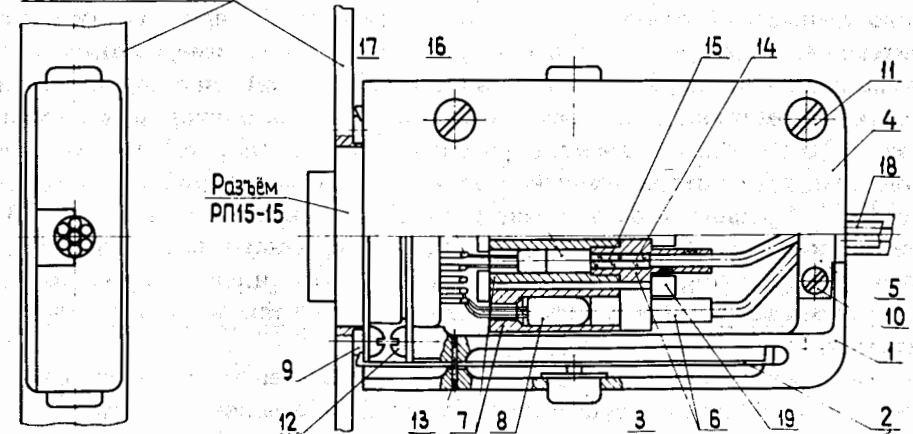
Многоконтактный активный разъемный соединитель на базе электрического разъема РП-15-15: (1 — корпус; 2 — пластинчатая пружина; 3 — кнопка; 4 — крышка корпуса; 5 — фиксатор ВОК; 6 — втулка; 7 — втулка для оптического компонента; 8 — светодиод; 9-13 — элементы крепления; 14 — ОВ; 15 — капилляр; 16 — фотодиод).
